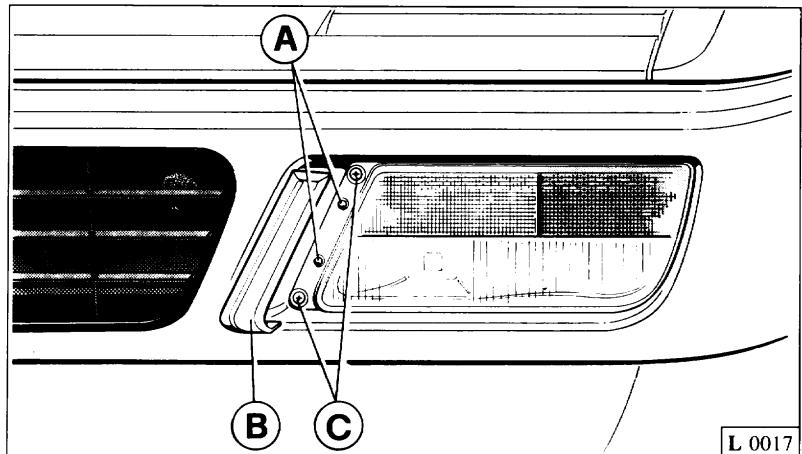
Sostituzione lampada fanale di posizione, direzione e lampeggio.
